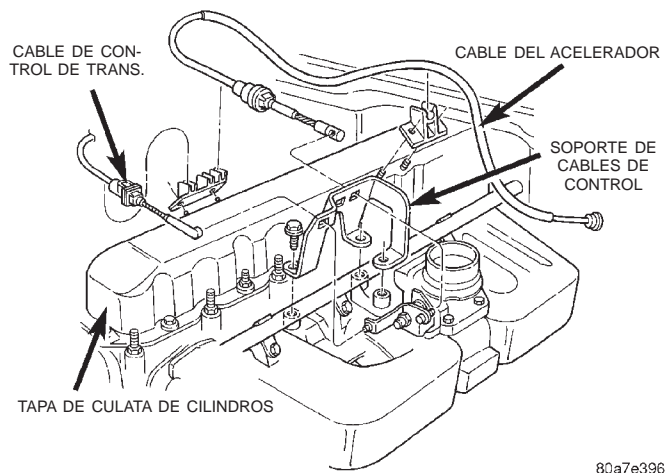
Tapa de la culata de cilindros del motor INSTALACION
